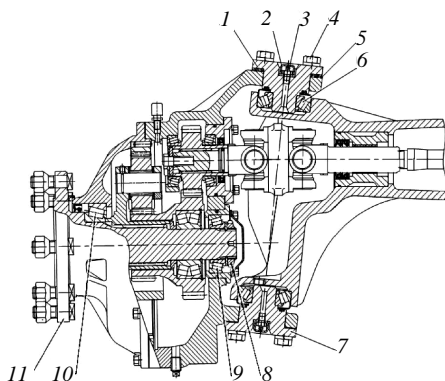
Регулировка осевого натяга в конических подшипниках шкворня: 1, 7 – оси поворотного шкворня; 2 – колпачок защитный; 3 – масленка; 4 – болт; 5 – прокладка регулировочная; 6, 9, 10 – подшипники роликовые конические; 8 – гайка; 11 – фланец колеса
